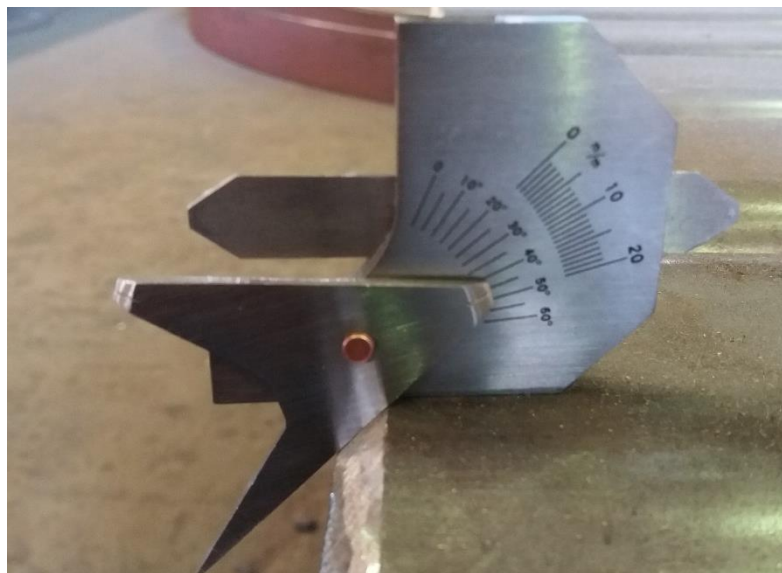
Medição do ângulo de chanfro para posterior soldagem (arquivo pessoal)
